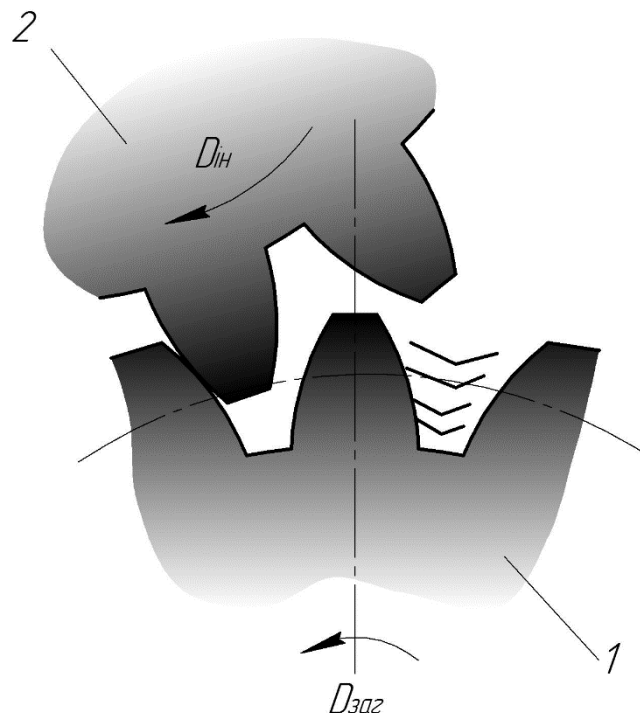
Схема безперервного руху заготовки зубчастого колеса при зубодовбанні: 1 – заготовка; 2 – довб'як
